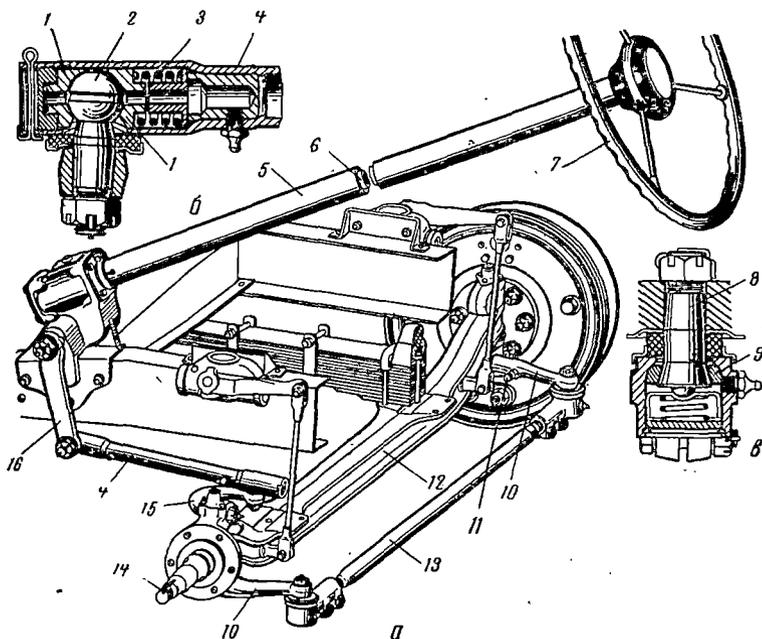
Рулевой привод автомобиля ГАЗ-51А:
